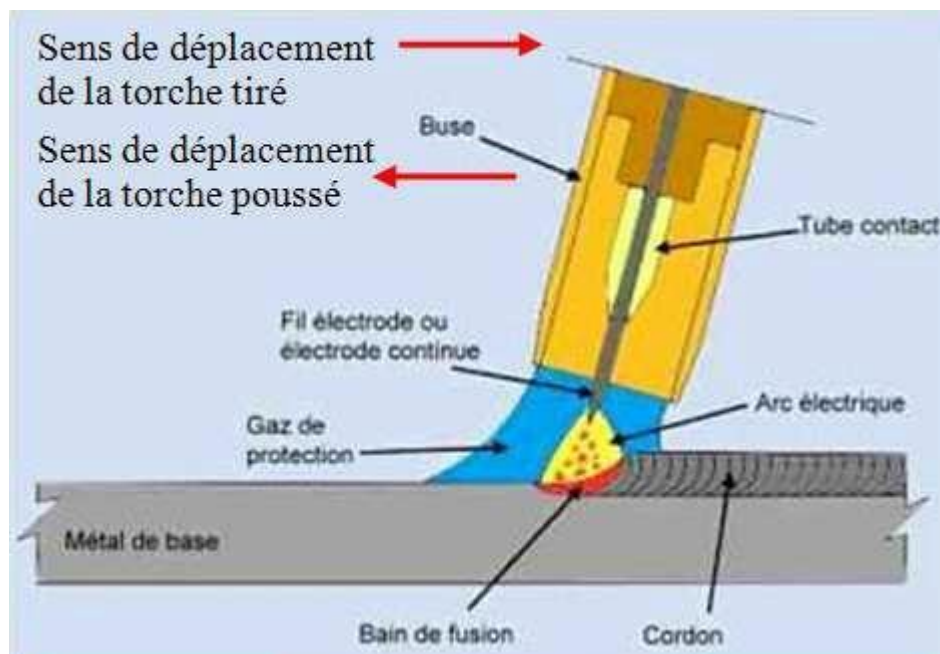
Procédés de soudage MIG/MAG
